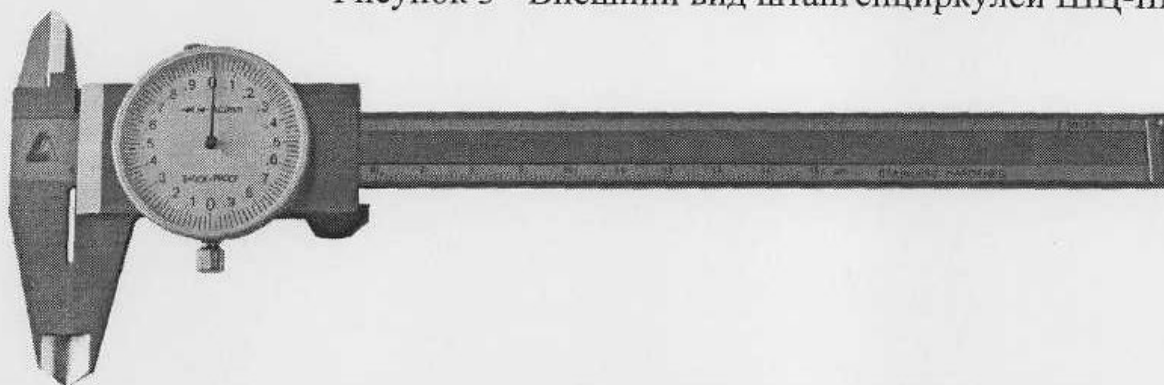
Внешний вид штангенциркулей ШЦ-К
